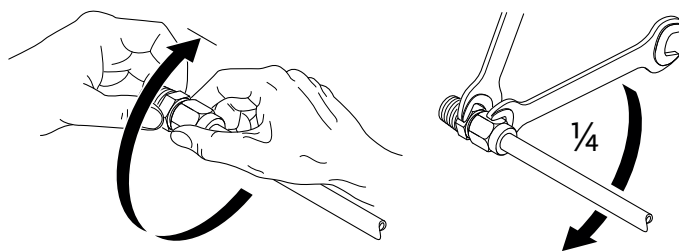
Дополнительный поворот резьбового соединения с обжимным кольцом на 1/4 оборота
